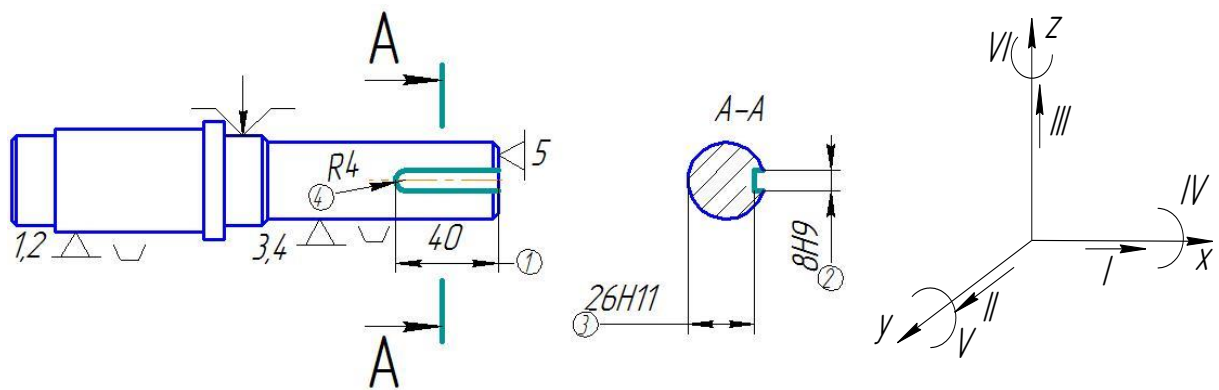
Схема базування заготовки при фрезеруванні шпонкового пазу
